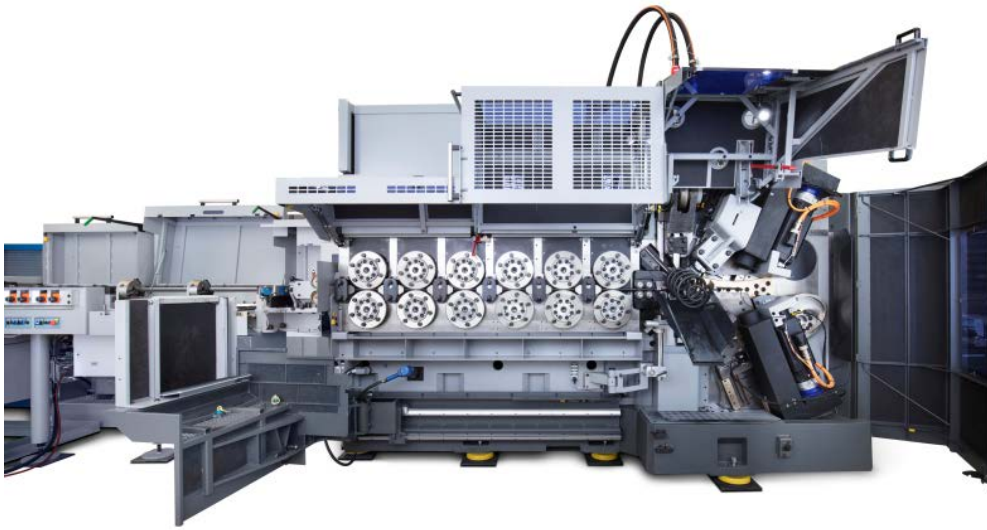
WAFIOS FUL 226 Federwindemaschine
